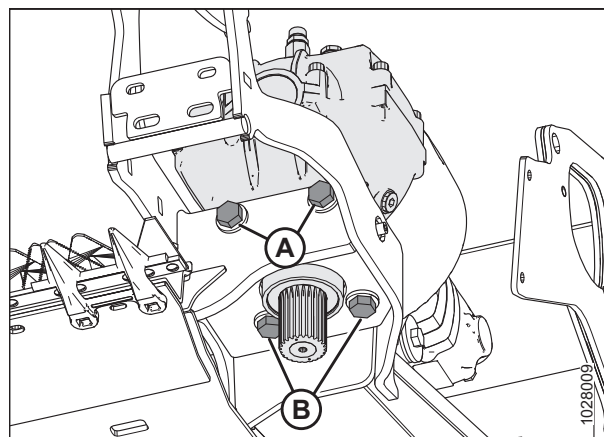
Редуктор привода ножа — вигляд знизу
